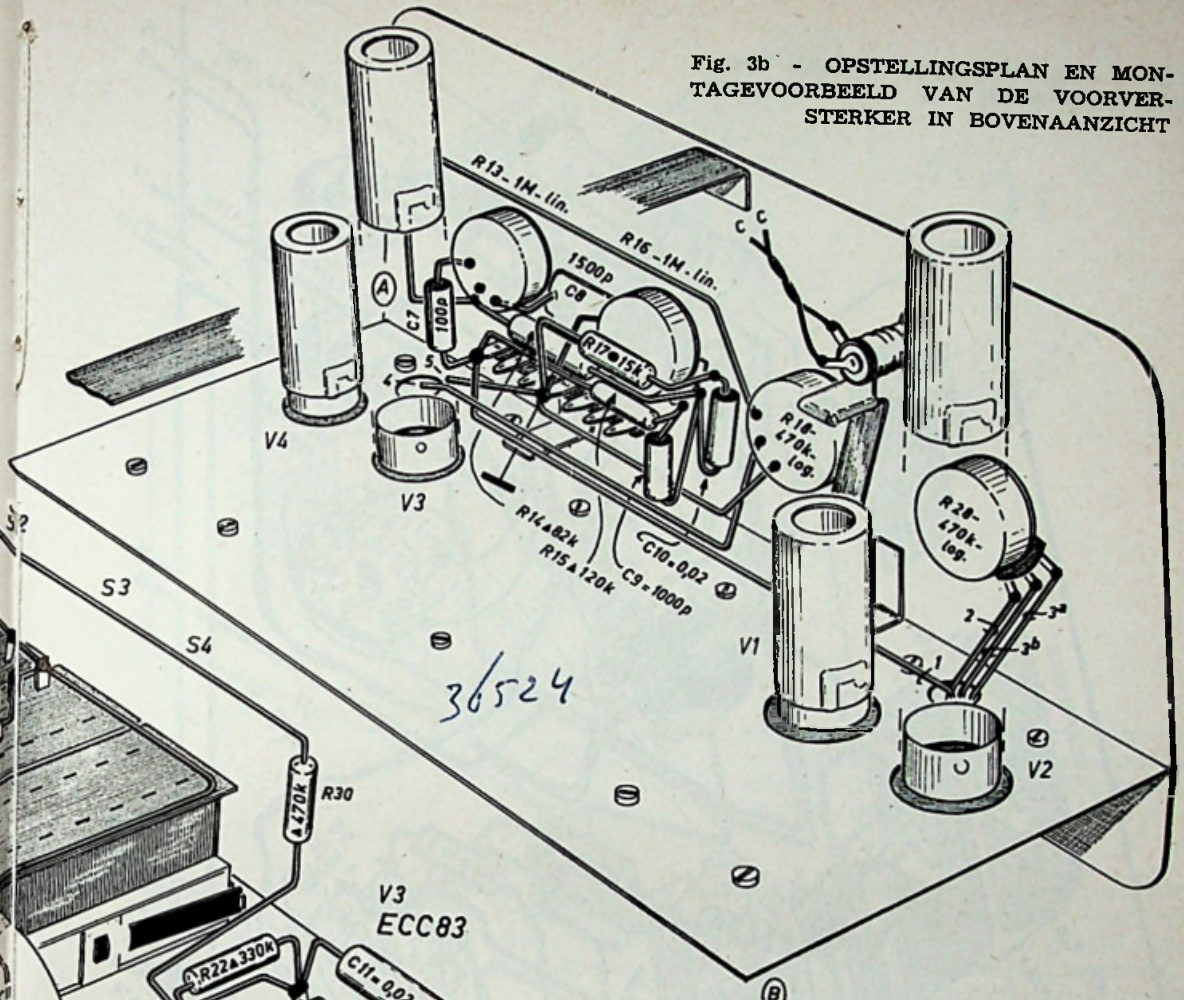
OPSTELLINGSPLAN EN MONTAGEVOORBEELD VAN DE VOORVERSTERKER IN BOVENAANZICHT
